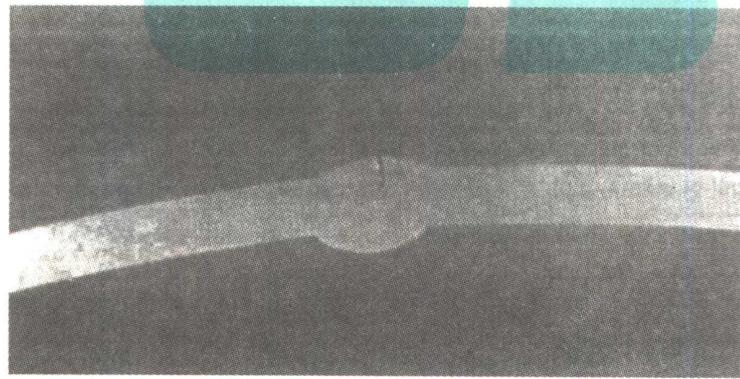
焊缝区裂纹——双面埋弧焊(I)
